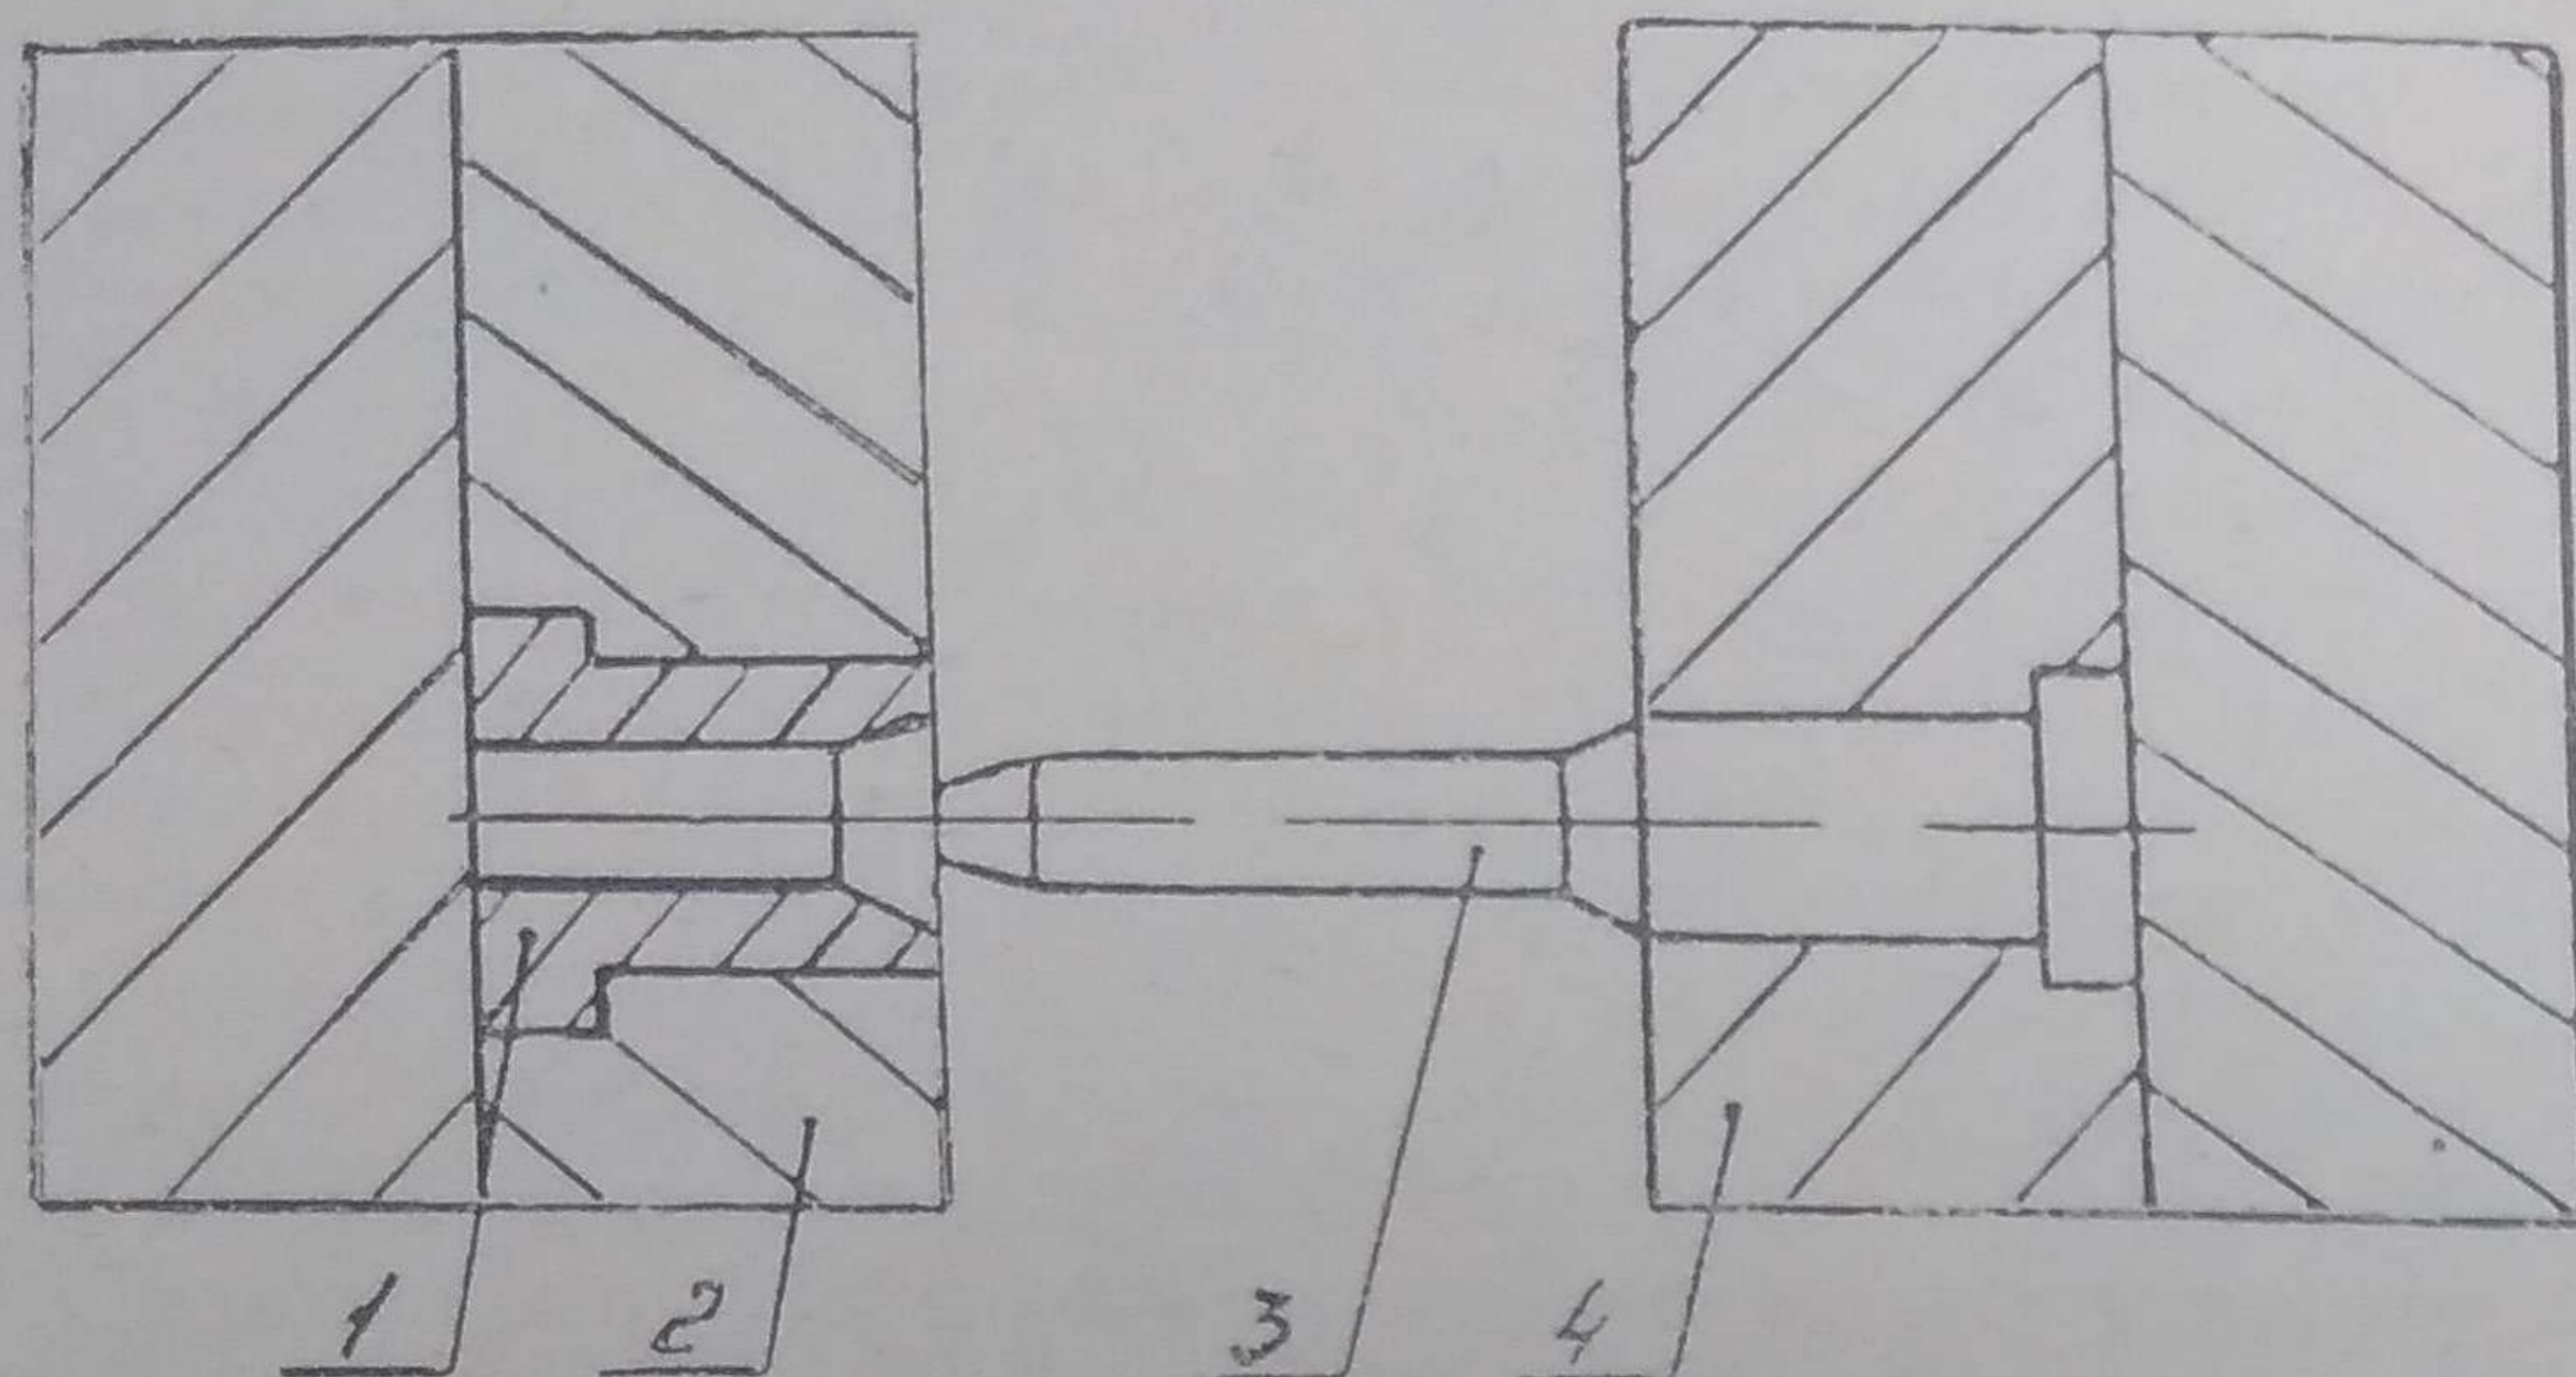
Узел центрирования полуформ коническими поверхностями: 1 — втулка центральная; 2 — обойма; 3 — колонка направляющая; 4 — обойма
